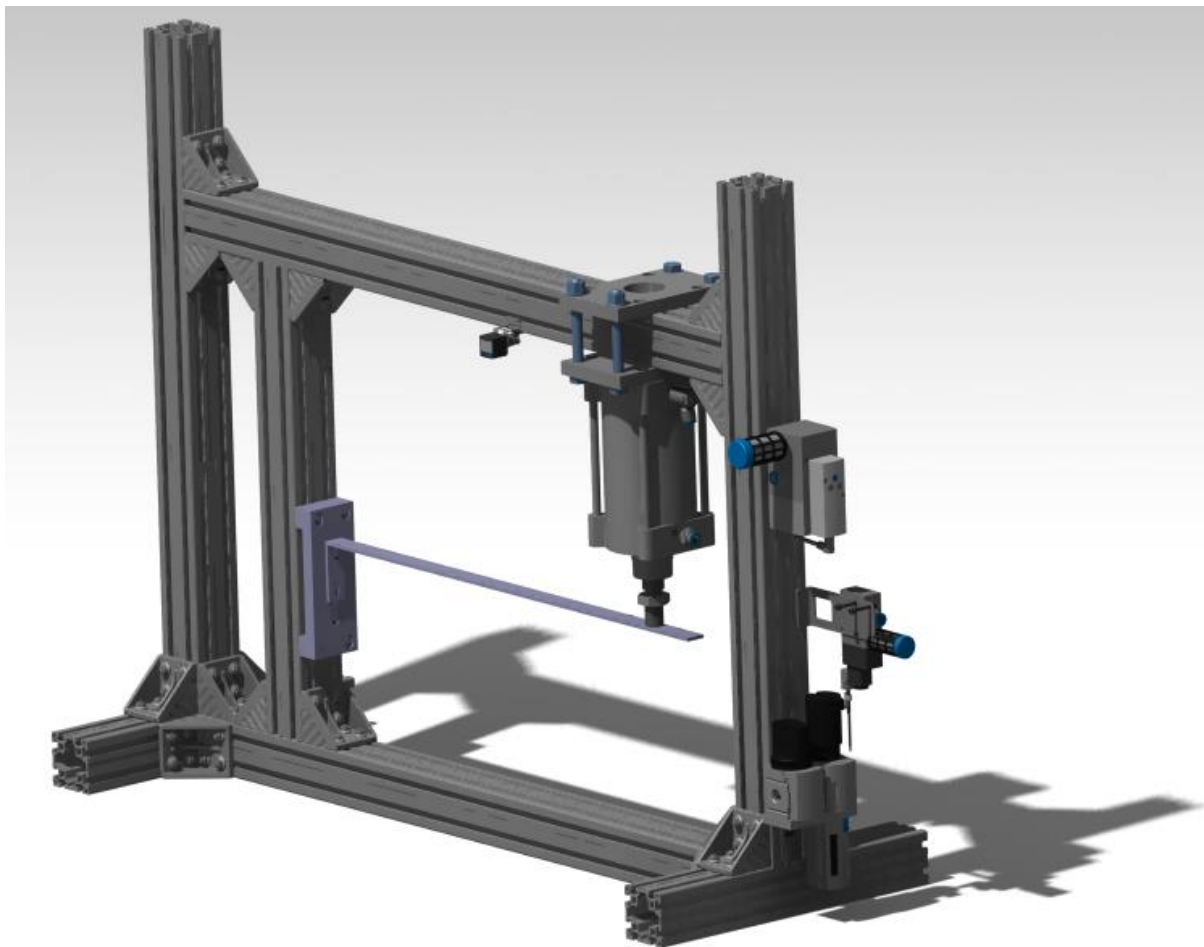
3D CAD model opreme za povezivanje pneumatskih komponenti [8]
